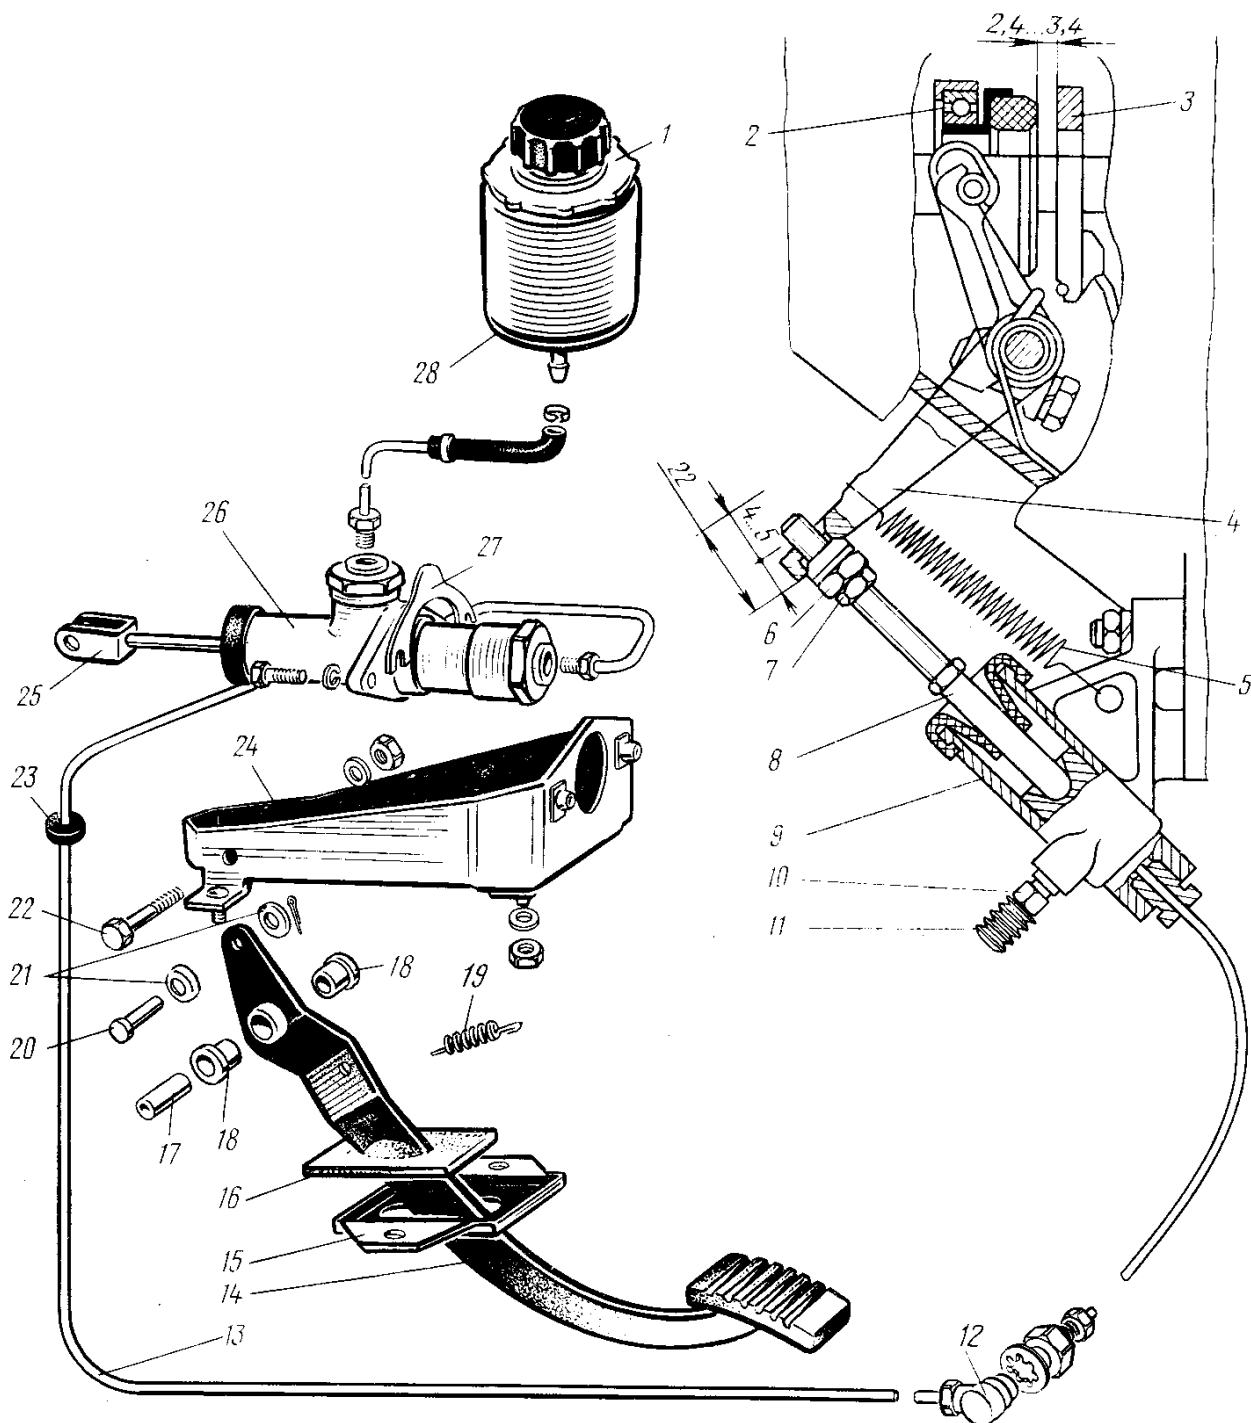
Гидравлический привод выключения сцепления: 1 — гайка крепления бачка; 2 — подпятник выключения сцепления; 3 — пята; 4 — рычаг оси; 5, 19 — пружины; 6 — регулировочная гайка; 7 — контргайка; 8 — толкатель; 9 — рабочий цилиндр; 10 — клапан выпуска воздуха; 11 — колпачок; 12 — соединительная муфта; 13 — трубка; 14 — педаль; 15 — каркас; 16 — уплотнитель; 17 — распорная втулка; 18 — втулка; 19 — пружина; 20 — палец; 21 — регулировочные шайбы; 22 — болт; 23 — уплотнитель; 24 — кронштейн; 25 — толкатель; 26 — главный цилиндр; 27 — регулировочная прокладка; 28 — бачок.
